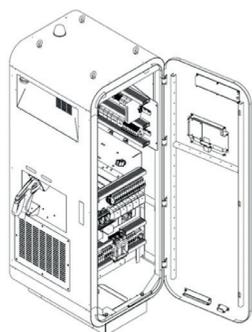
Исполнение корпусов ЭЗС модели EVT-FCB
